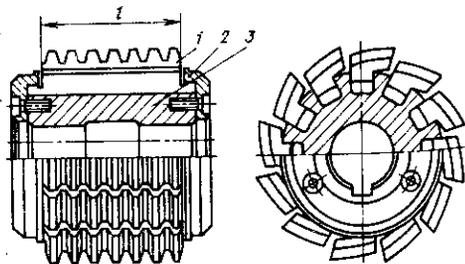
Сборная червячная фреза с поворотными вставными рейками
